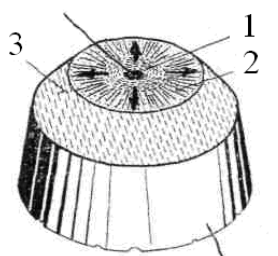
Схема будови поверхні злому циліндричного гладкого зразка:
